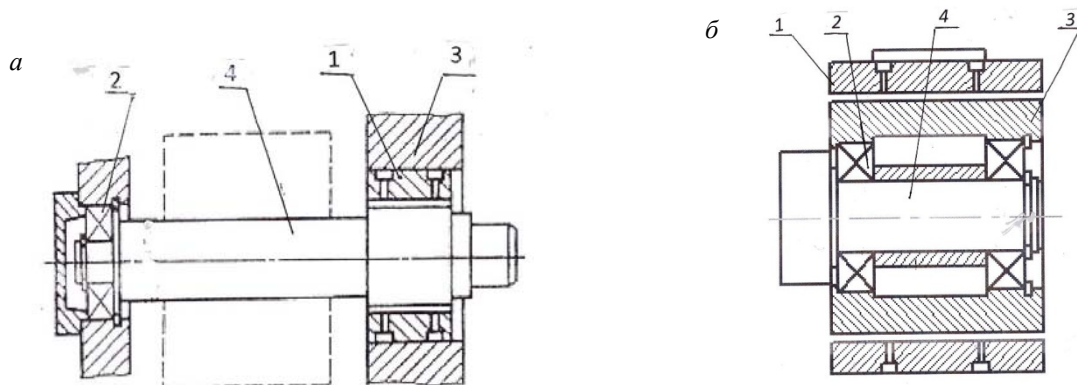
Схемы совмещенной установки газового подшипника и подшипника качения: 1 – газовый подшипник; 2 – подшипник качения; 3 – корпус, 4 – шпиндель; а – раздельная; б – параллельная
